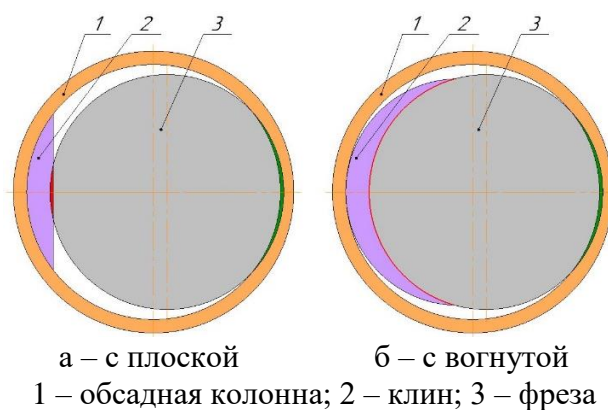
Величина контактной поверхности клина с фрезой при различном конструктивном исполнении отклоняющей поверхности клина
